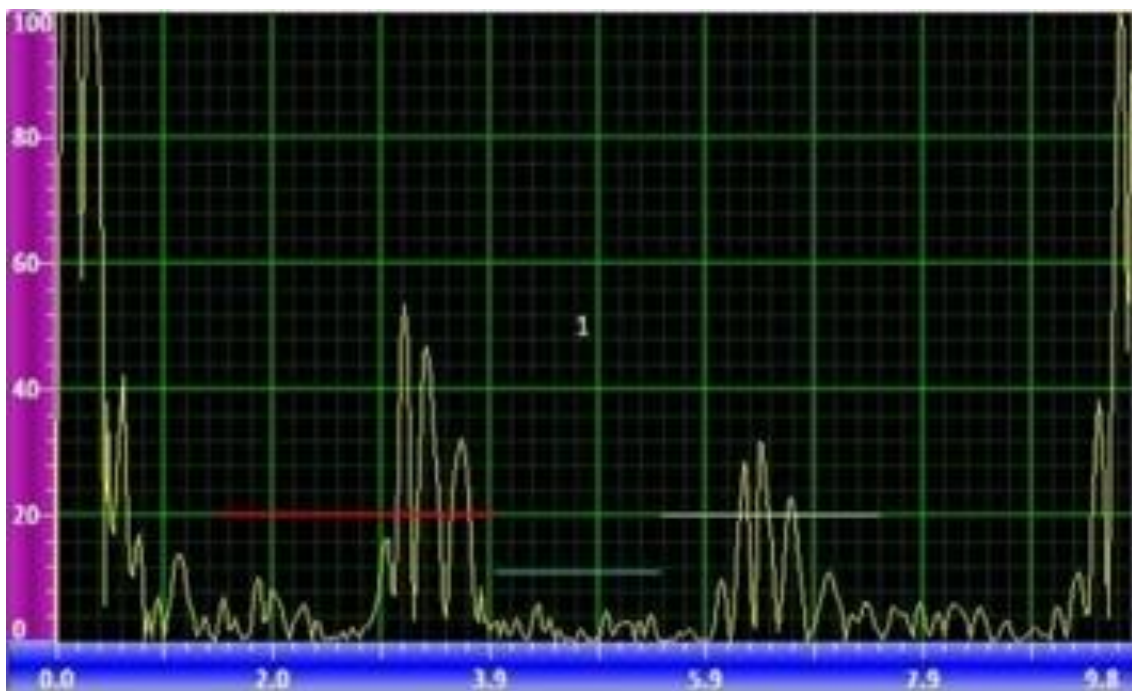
Спектр сварной точки без дефекта. Хорошая сварка
